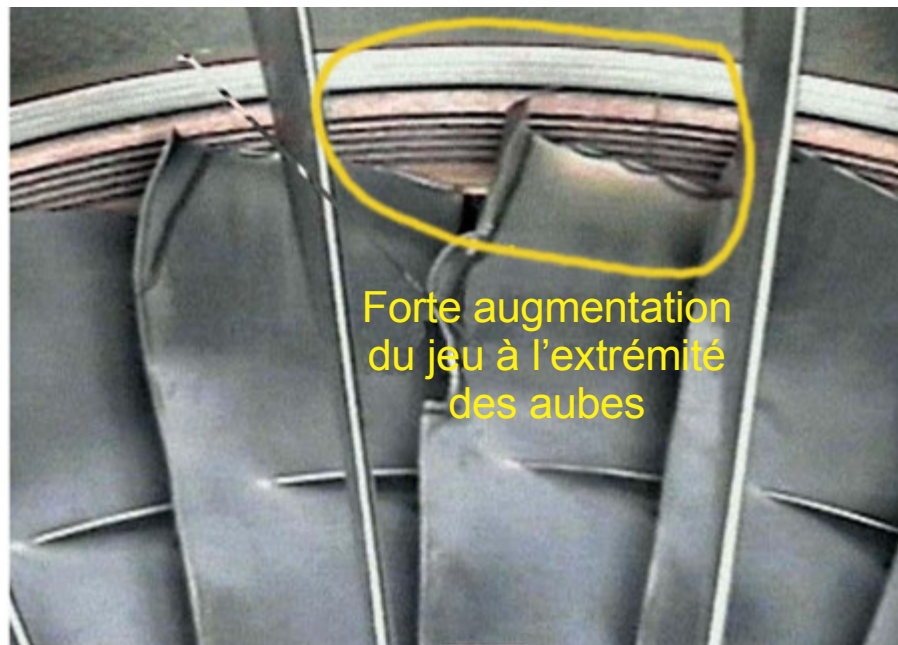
Augmentation du jeu à l'extrémité des aubes de la soufflante causée par le frottement
